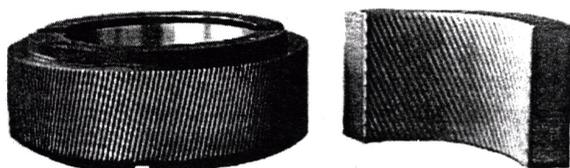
Накатной инструмент (ролик и сегмент) для изготовления неизвлекаемого крепежа
